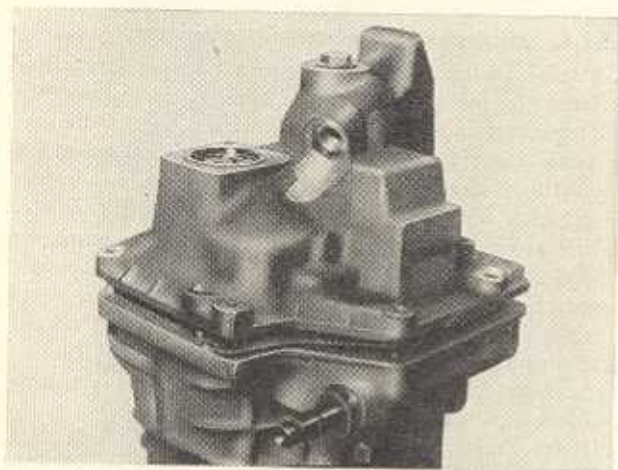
Hinteres Getriebegehäuse aufsetzen
